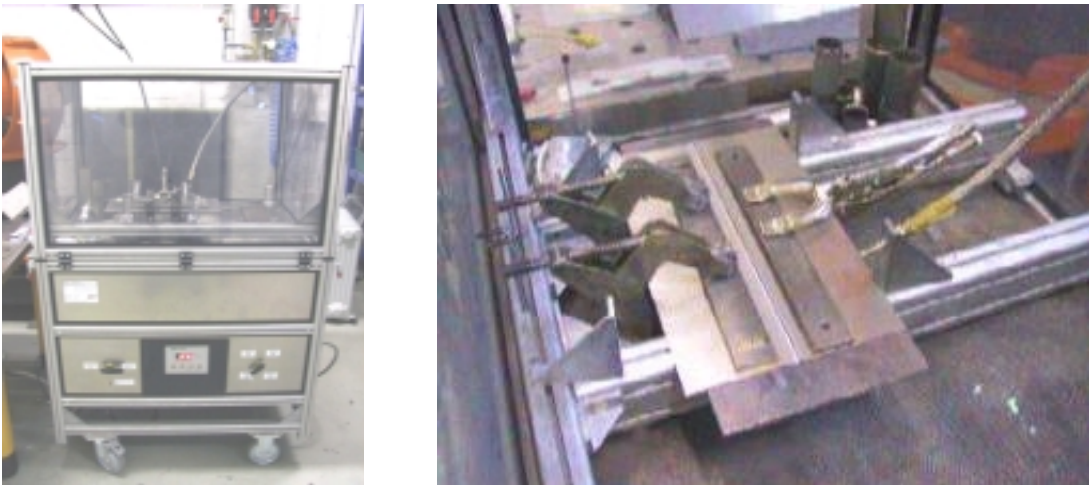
Esquerda câmara de soldagem e direita fixação das placas dentro da câmara.
